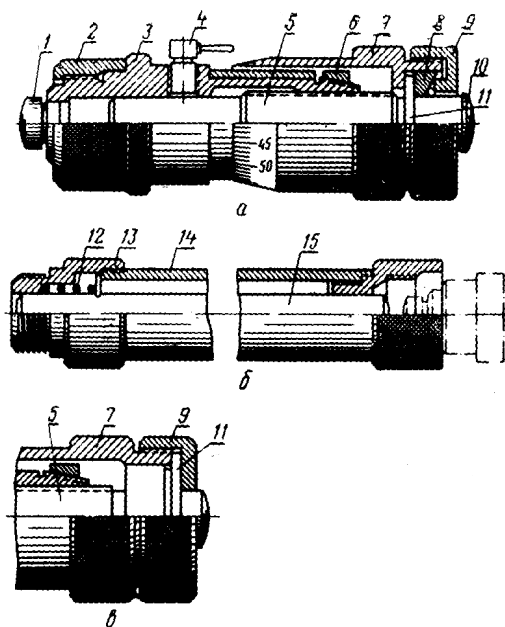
Микрометрический нутромер: 1 и 10 – сферические наконечники; 2 – предохранительная гайка; 3 – стебель; 4 – стопорный винт; 5 – микровинт; 6 – регулировочная гайка; 7 – барабан; 8 – разрезное кольцо; 9 – установочный колпачок; 11 – буртик; 12 – пружина; 13 – предохранительная головка; 14 – предохранительная трубка; 15 – удлинитель
